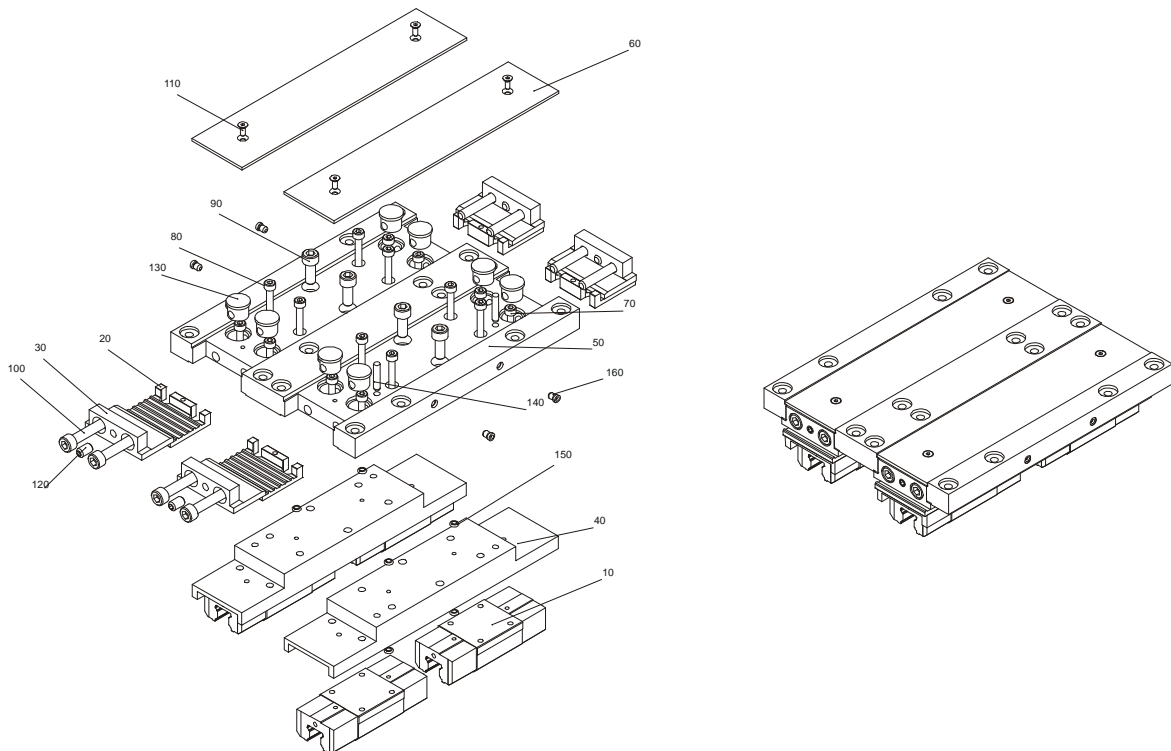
Modul 160/15, Schlitten komplett, Explosionszeichnung
